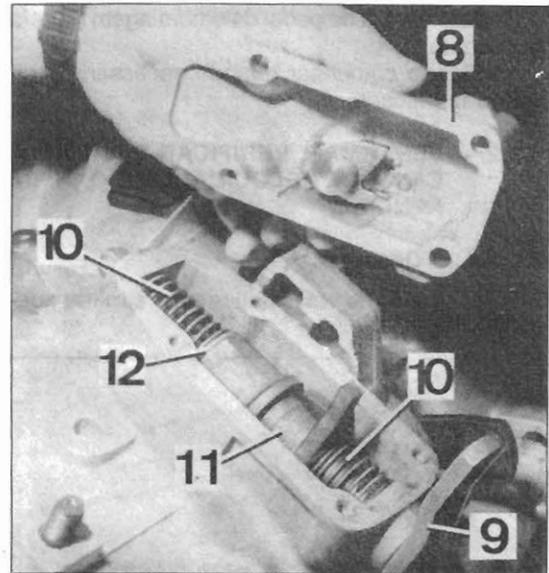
Desmontagem da tampa do mecanismo de seleção/comando
